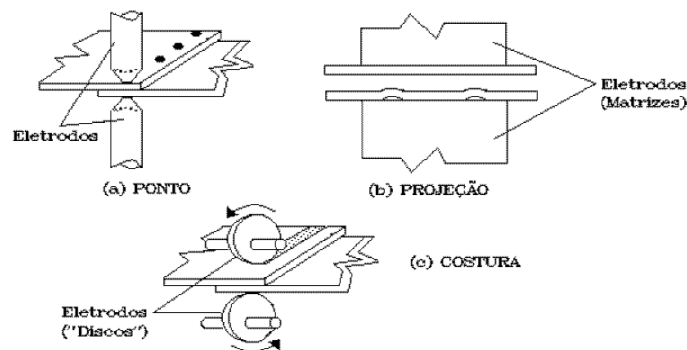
Principais Métodos de Soldagem por Resistência Elétrica – (a) Soldagem por Pontos, (b) Soldagem por Projeção, (c) Soldagem por Costura
